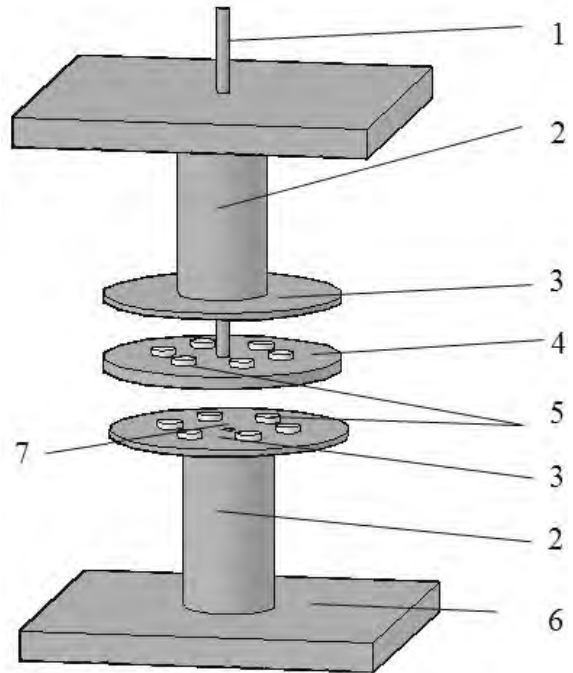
Конструкция компенсатора жесткости на основе супермагнитов: 1-шток; 2-металлическое основание; 3-металлический диск; 4-якорь; 5-неодимовые магниты; 6-основание; 7-отверстие для штока
